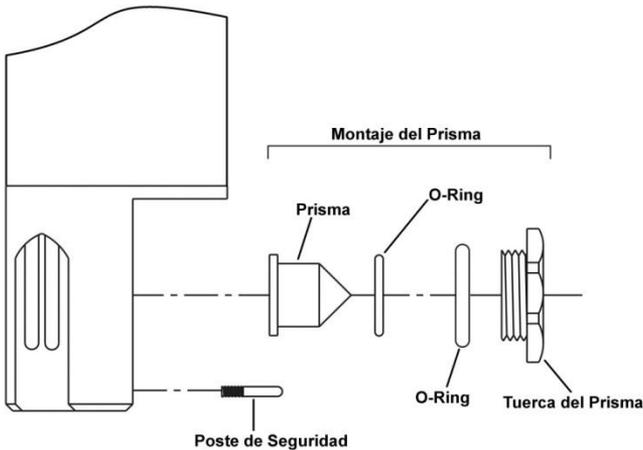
Montaje del Prisma en una Large Diameter Chemical Interface Probe
